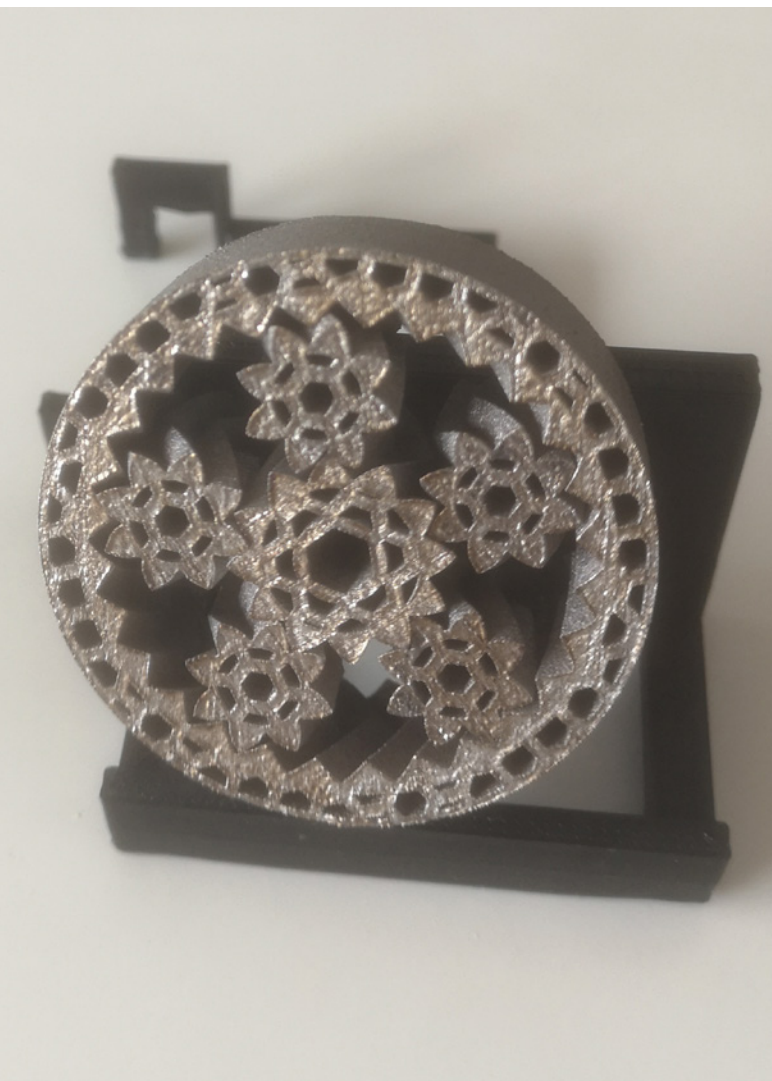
Gedrucktes Getriebe als Demonstrator für Funktionsintegration, Werkstoff H13 (1.2344), gefertigt auf Alpha Laser AL3D 250 im Smart Manufacturing Lab der Hochschule München, Außendurchmesser: 45 mm
